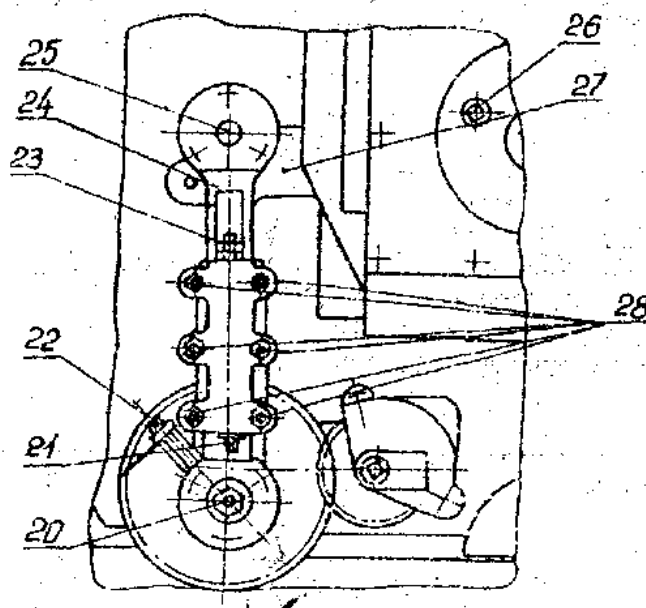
Кривошипно-шатунный механизм главного привода
